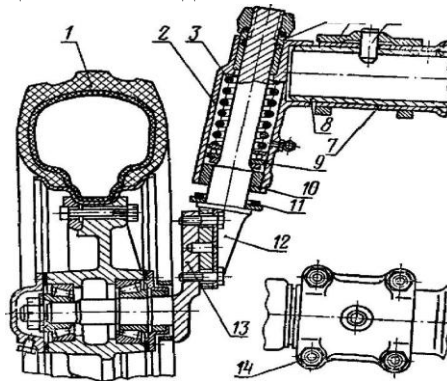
Передня незалежна підвіска трактора (*T-40M*): 1 - шина; 2 - кулак; 3 - пружина; 4,10 - втулки; 5 - бугель; 6 - штифт; 7 - кожух; 8 - труба; 9 упорний підшипник; 11 - буфер; 12 - поворотна цапфа; 13 - фланец; 14 – болт.
